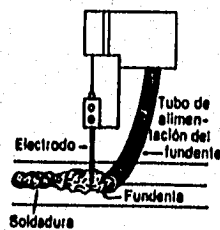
Proceso de soldadura de arco sumergido.
